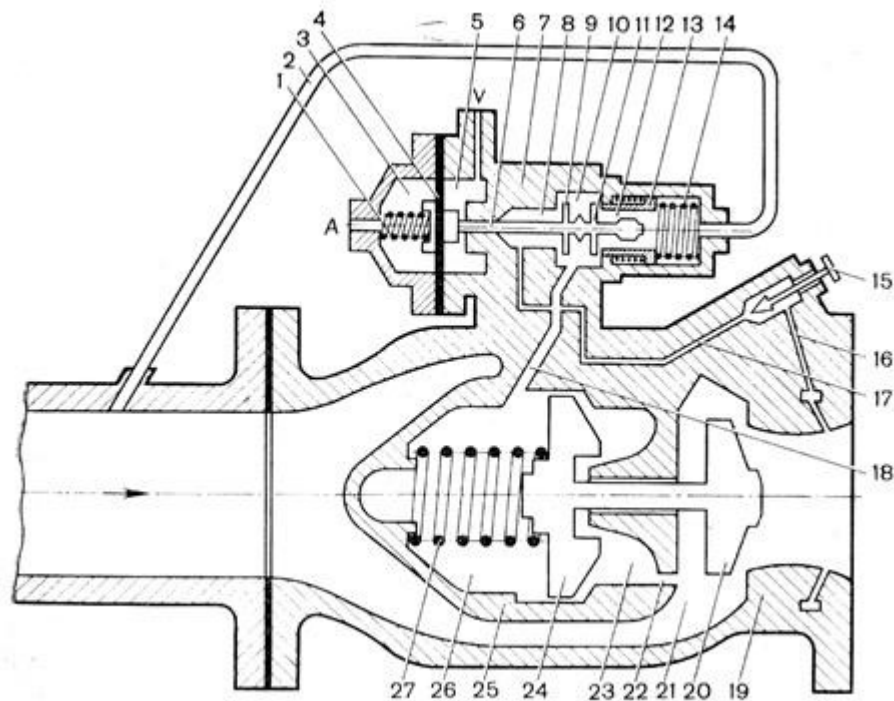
Схема регулятора тиску заправного агрегату
